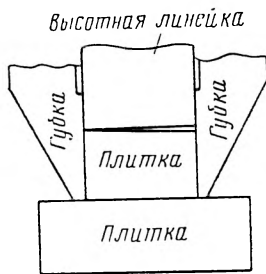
Проверка положения торцов губок и высотной линейки штангензубомера с помощью плиток
